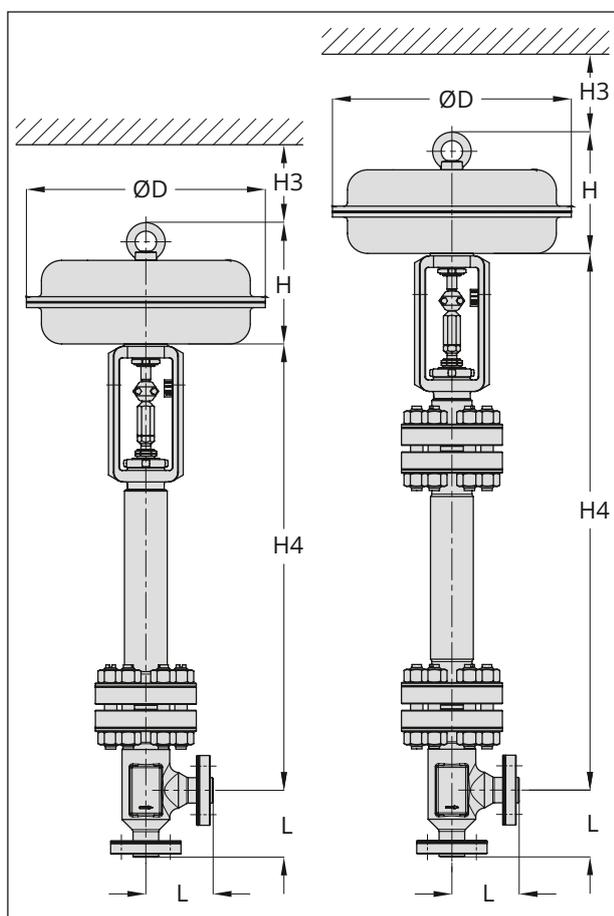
Typ 3259-1 · mit Isolierteil (links) · mit Balgteil (rechts)
